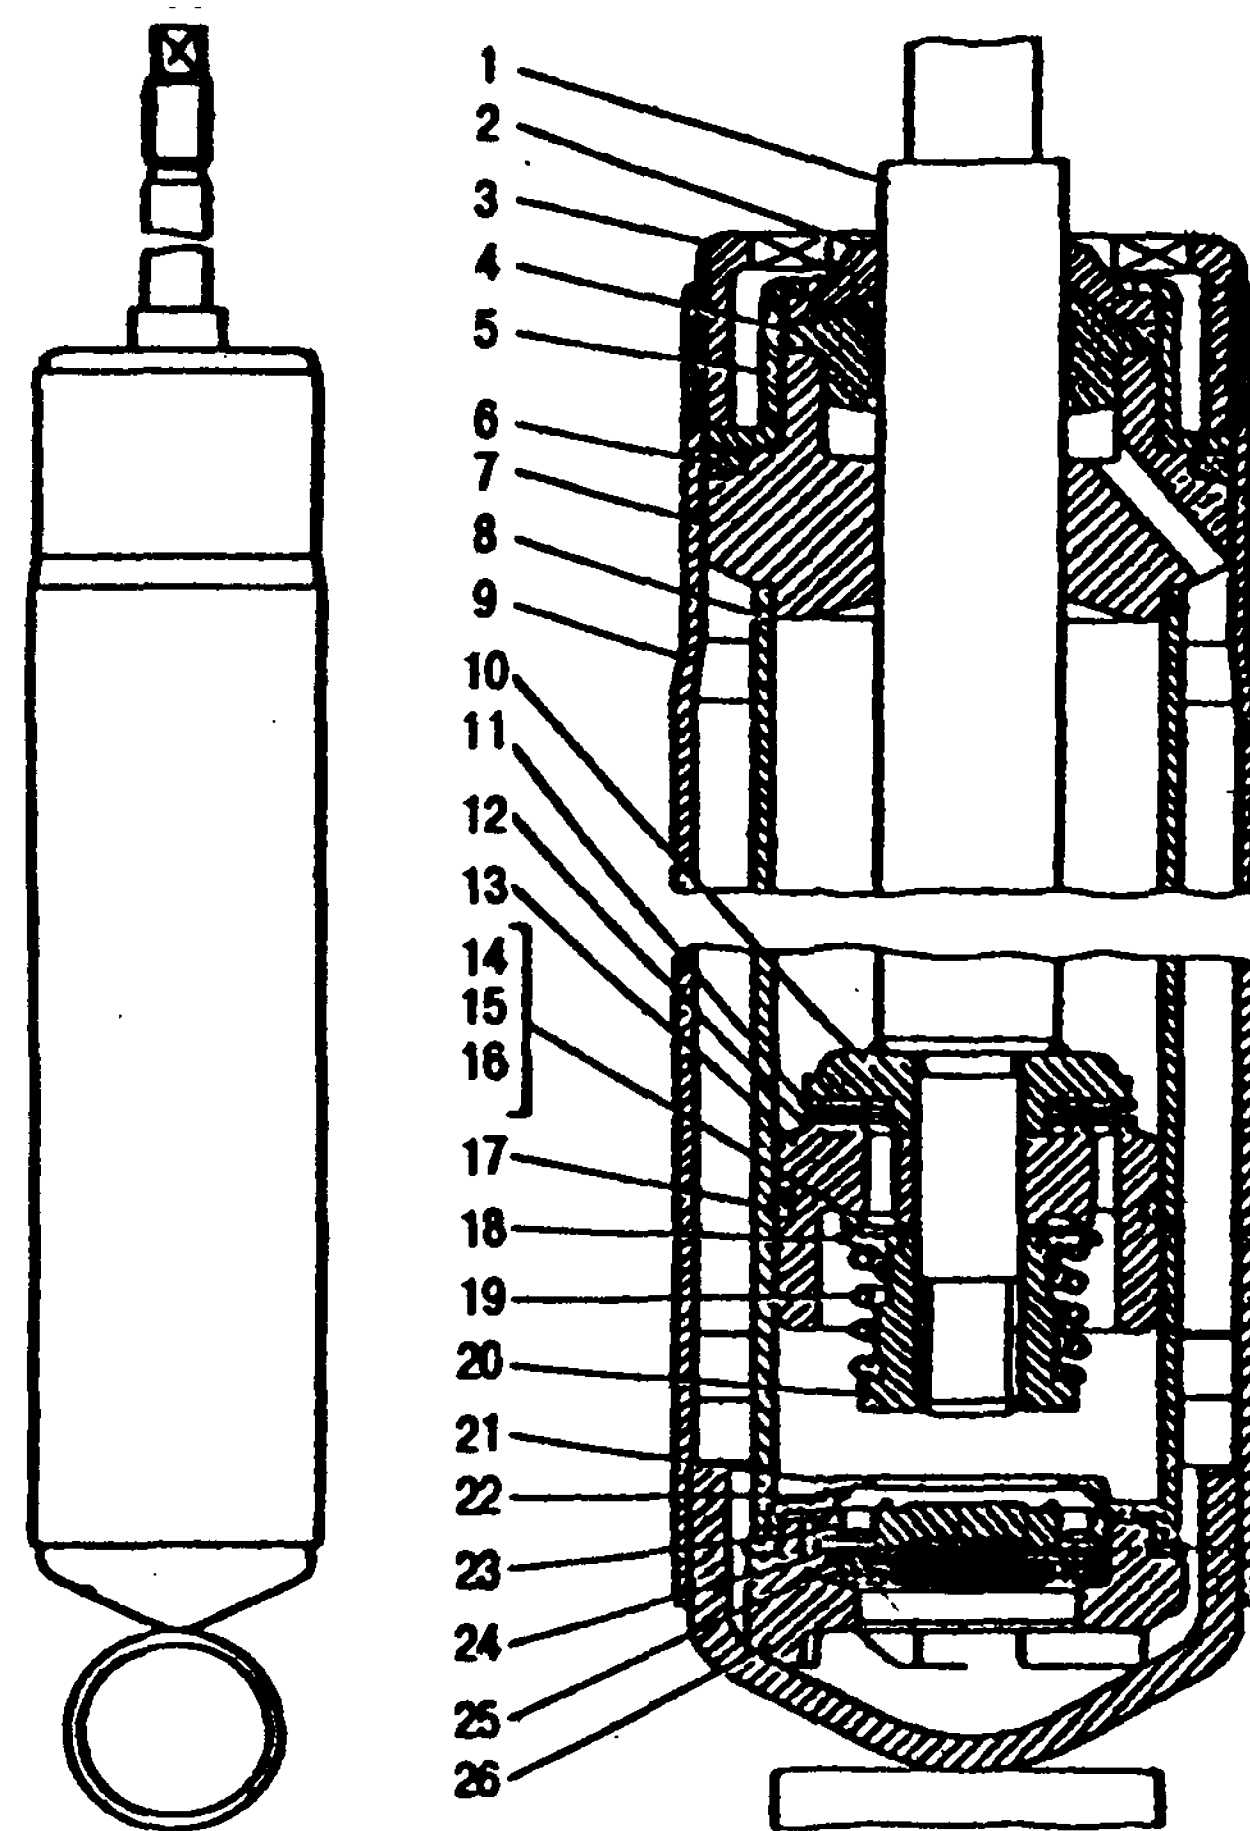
Амортизатор: 1 - шток; 2 - защитное кольцо; 3 - гайка резервуара; 4 - манжета штока; 5 - обойма манжеты; 6 - уплотнительное кольцо; 7 - направляющая втулка штока; 8 - цилиндр; 9 - резервуар; 10 - ограничительная тарелка; 11 - пружина перепускного клапана; 12 - тарелка перепускного клапана; 13 - поршень; 14 - дроссельный диск; 15 - диск клапана отдачи; 16 - шайба; 17 - кольцо поршня; 18 - упорная тарелка; 19 - пружина клапана отдачи; 20 - гайка; 21 - обойма клапана сжатия; 22 - пружина впускного клапана; 23 - тарелка клапана сжатия; 24 - дроссельный диск; 25 - диск клапана сжатия; 26 - корпус клапана сжатия
